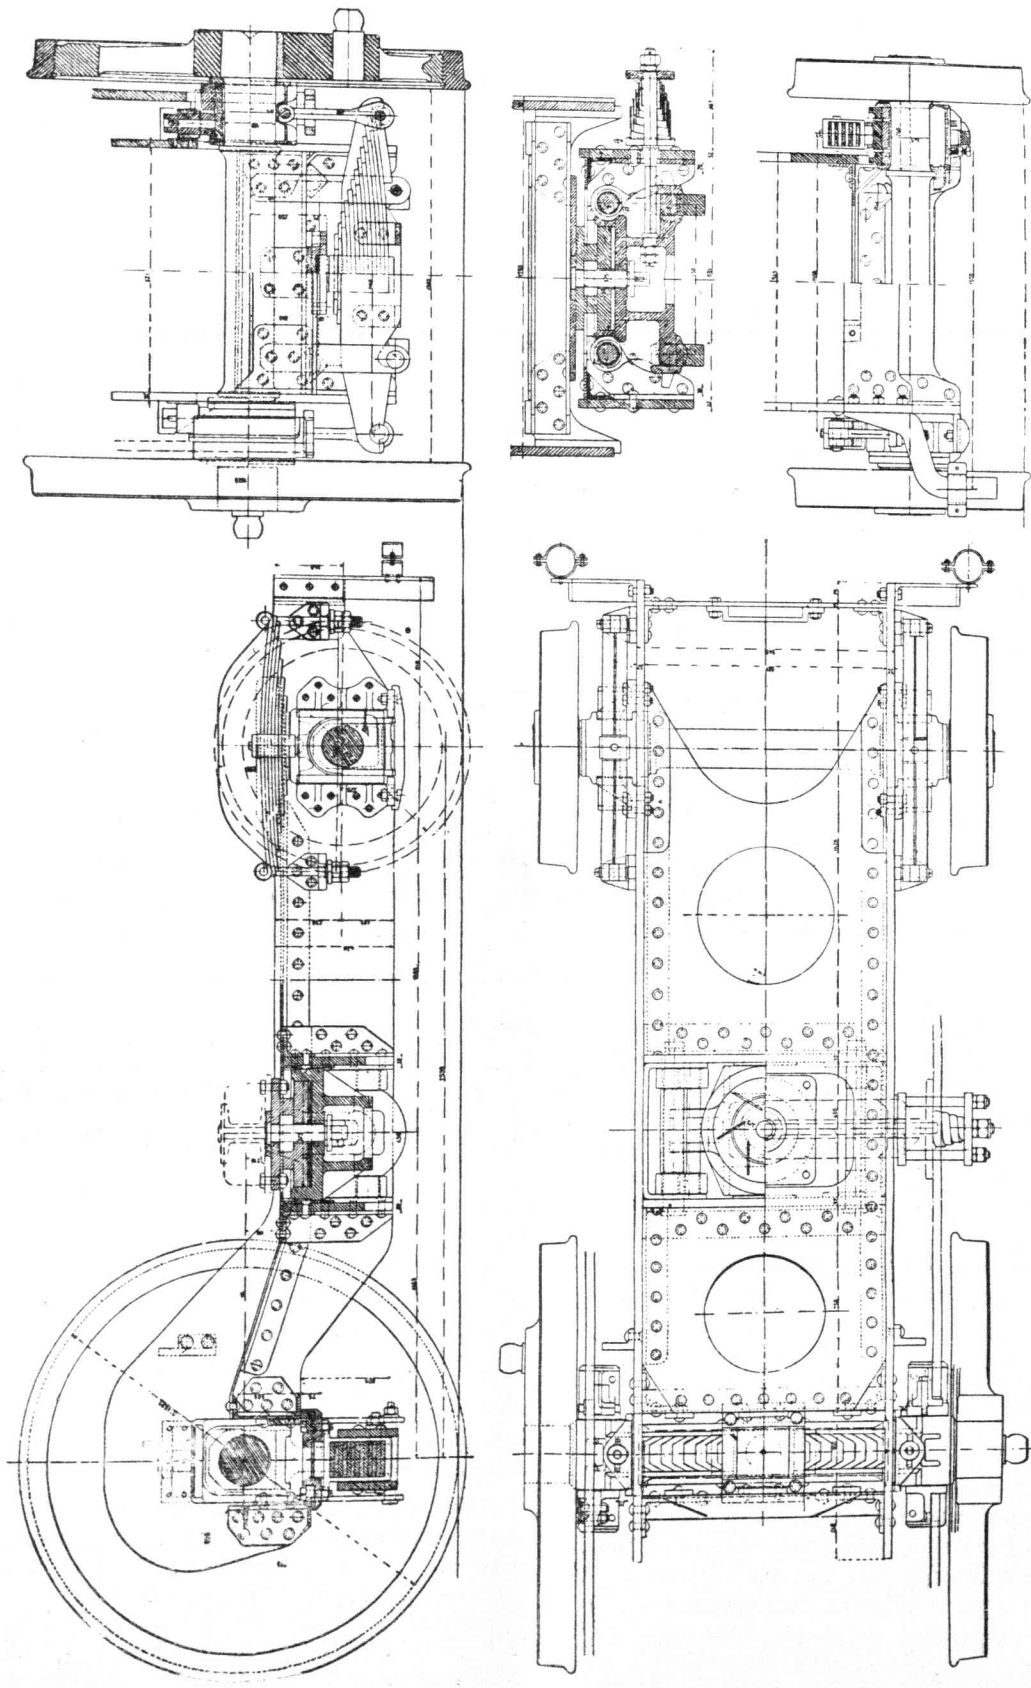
Detailzeichnung des «Carello italiano». Ausführung für die Gruppe 380 der R. A. (jetzt Gruppe 600 der F. S. J.).
